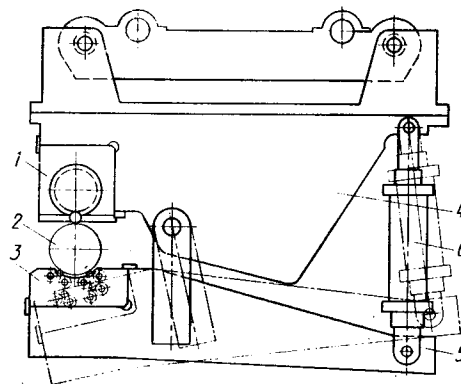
Схема рабочего органа станка для упрочнения галтели одной из шеек коленчатого вала:
